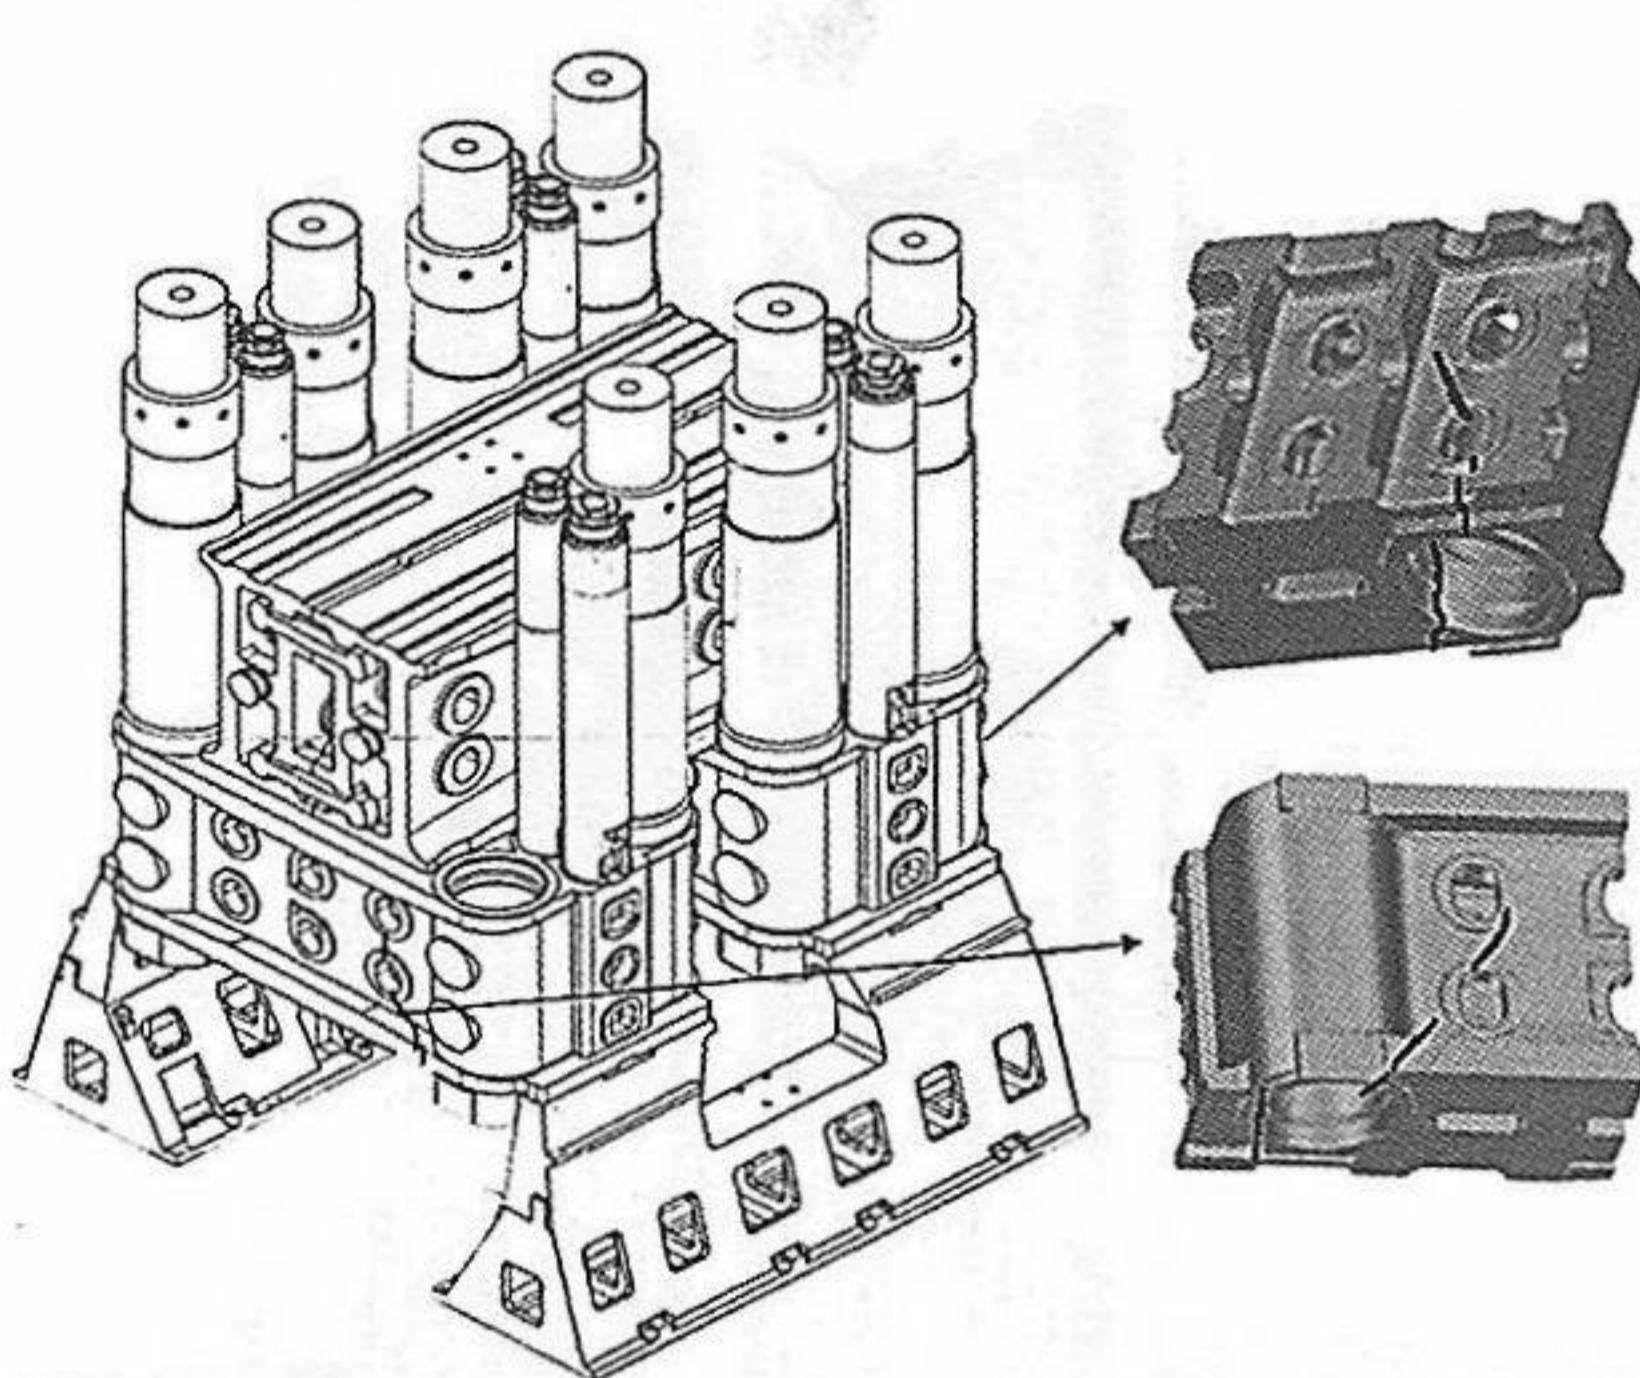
Схема разрушения поперечных балок основания пресса усилием 50 000 тс
